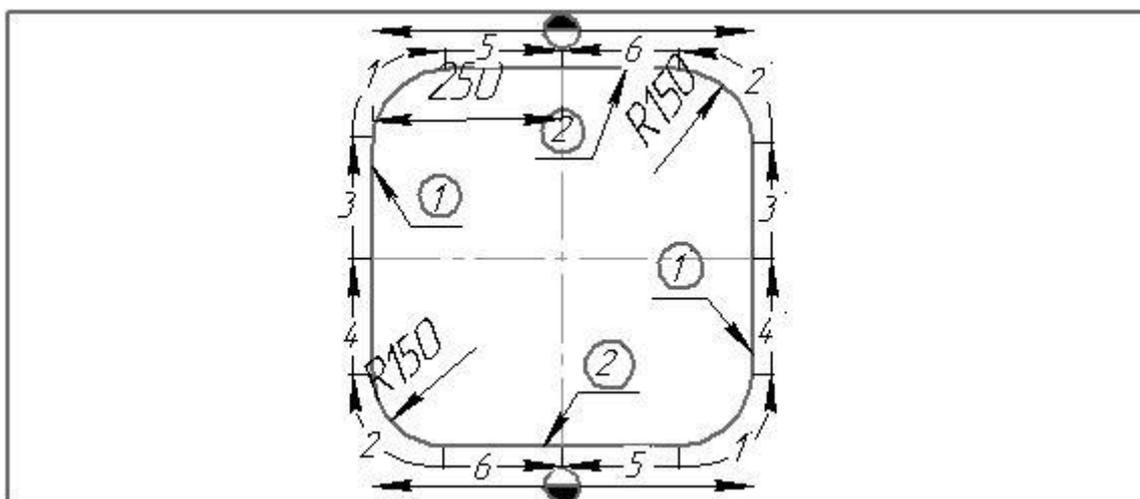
Схема сварки ремонтной вставки «от центра до края»
